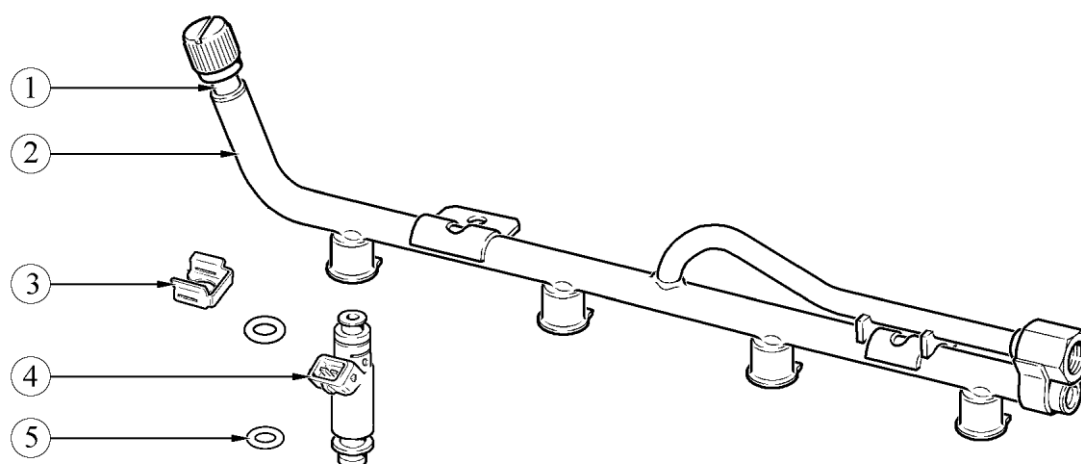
Рампа форсунок в сборе двигателя 21126:
